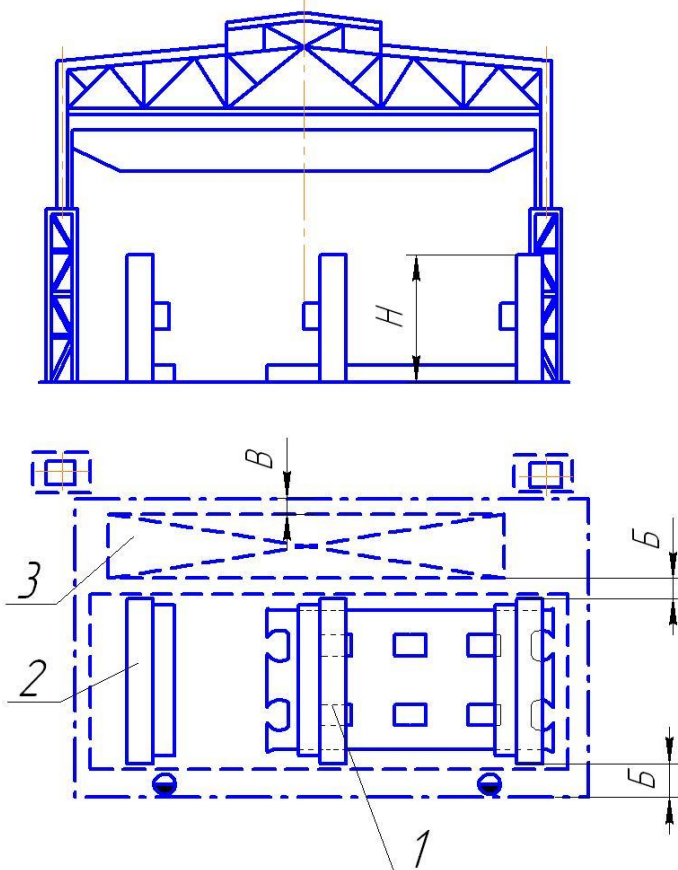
Размещение двухстороннего торце-фрезерного станка в поперечном пролете: 1 – подвижная часть станка с фрезой; 2 – неподвижная часть станка с фрезой; 3 – место складирования; $B = 800$ мм; $b = 500$ мм
